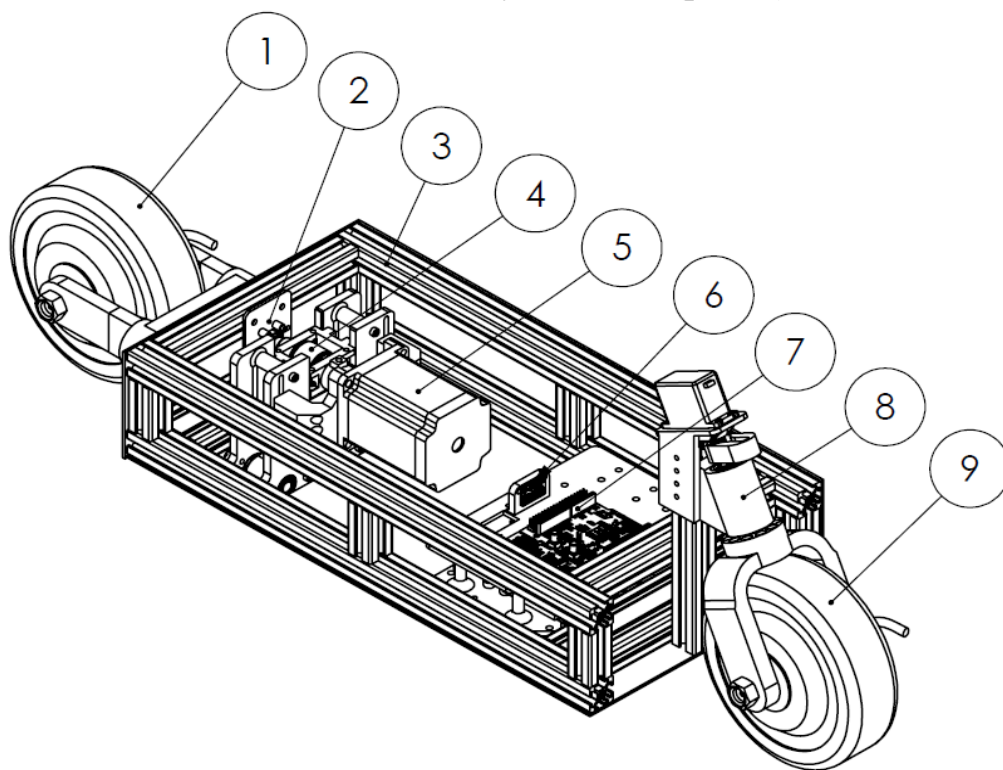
3D-модель пристрою для транспортування малогабаритних вантажів: 1) заднє приводне мотор-колесо; 2) датчик повороту заднього колеса; 3) рама пристрою; 4) механізм балансування; 5) кроковий електродвигун; 6) гіроскоп; 7) плата керування; 8) поворотна стійка з механізмом повороту колеса; 9) переднє приводне мотор-колесо
